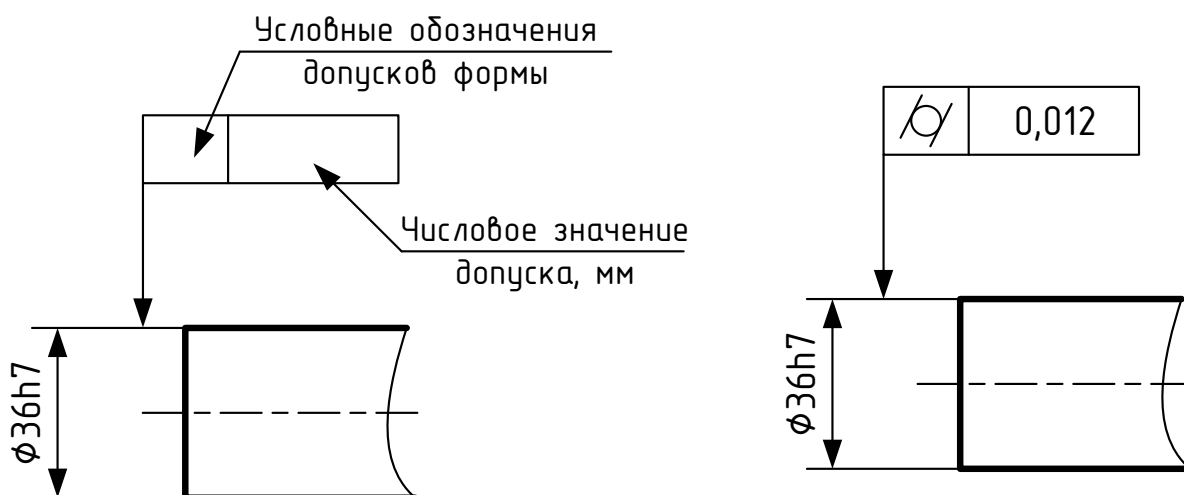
Обозначения допусков формы и расположения на чертеже
